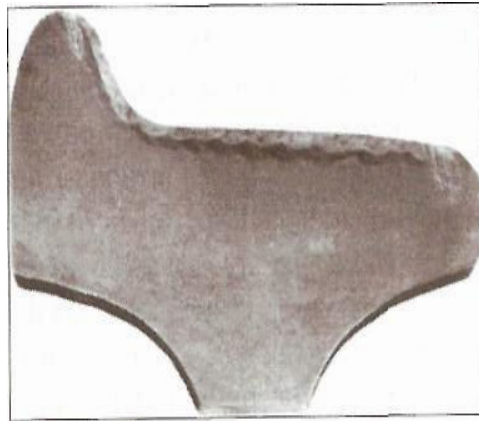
Макроструктура наплавлення поверхні катання колеса зварювальним дротом Св-08Г2С діаметром 3 мм [5]
